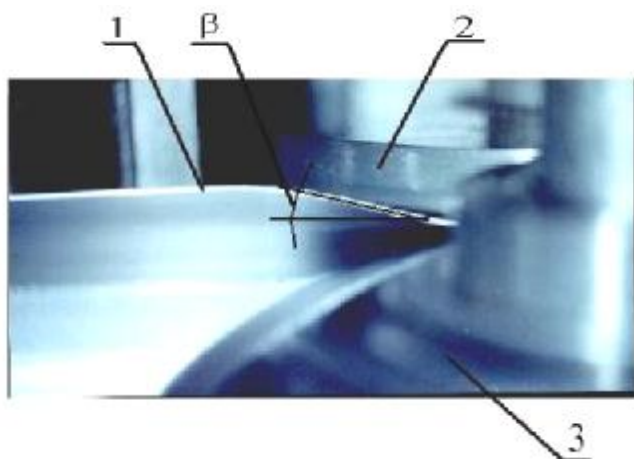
Заход торца профиля в роликовой калибр: 1 – торец профиля; 2 – вертикальный бурт нижнего ролика; 3 – верхний ролик;
